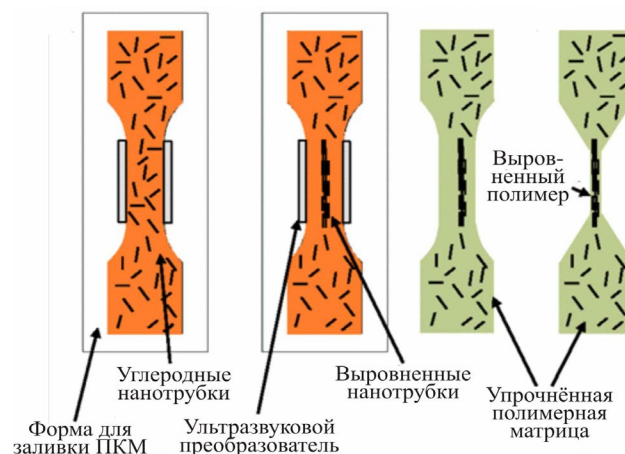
Изготовление образца ПКМ для испытаний на растяжение
